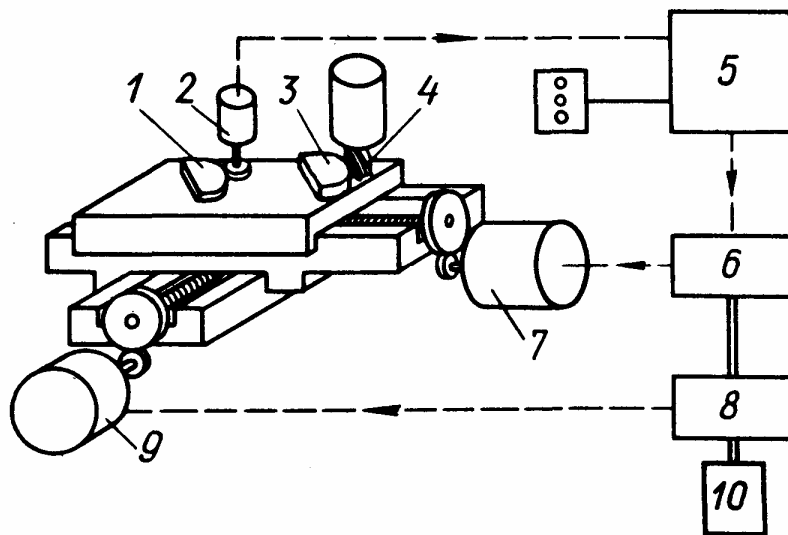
Схема двокоординатного копіювально-фрезерного верстата: 1 – копій; 2 – слідкувальний пристрій; 3 – заготовка; 4 – фреза; 5 – підсилювач; 6 – генератор; 7, 9 – слідкувальні електродвигуни подачі; 8 – генератор; 10 – електродвигун привода головного руху
